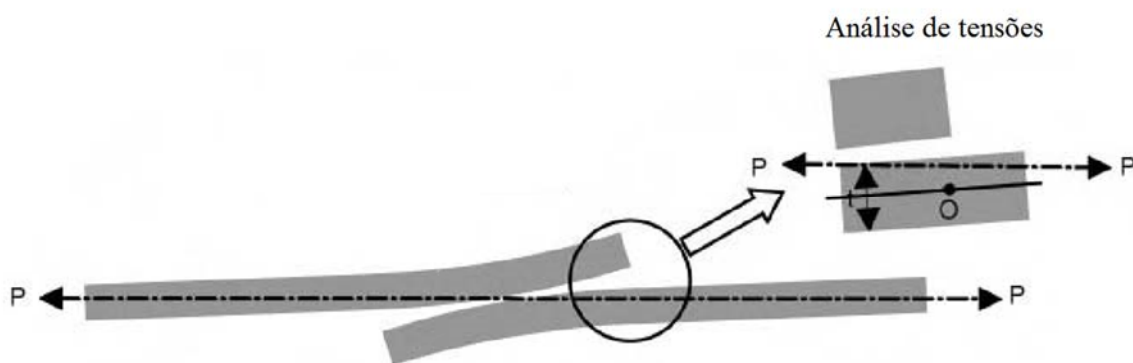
Deflexão transversa da junta de sobreposição simples [13]
